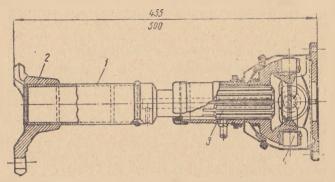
Передний пижими карданный вал «ЗИС-11».
